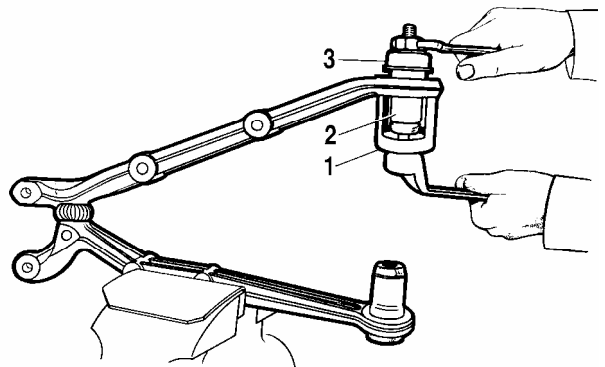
Выпрессовка шарниров нижнего рычага:
